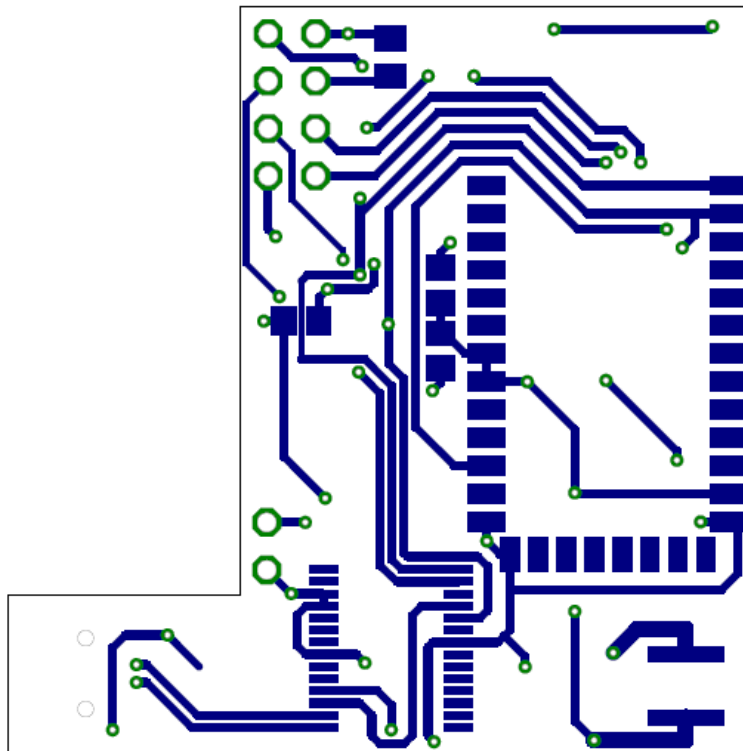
Layout WristPCB gespiegelt Bottom
